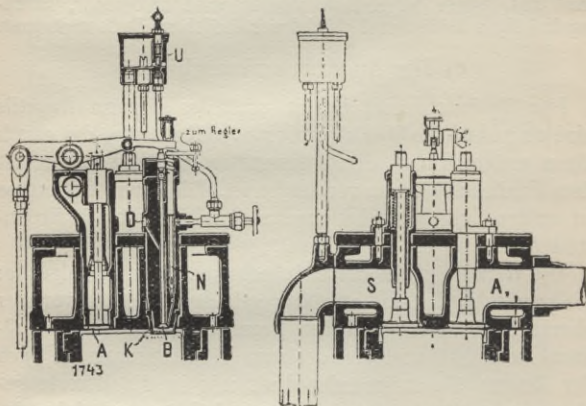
Brons-Maschine der Gasmotorenfabrik Deutz; Schnitt durch den Zylinderkopf.
